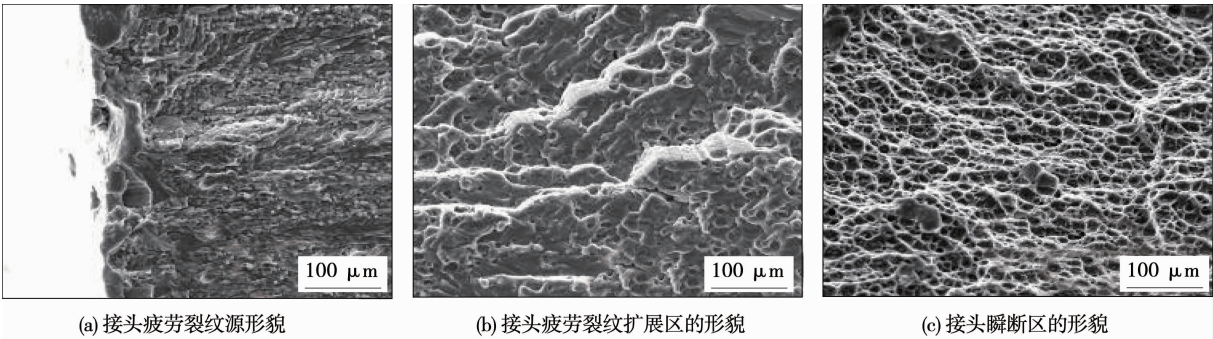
静轴肩搅拌摩擦焊接头疲劳断口形貌
